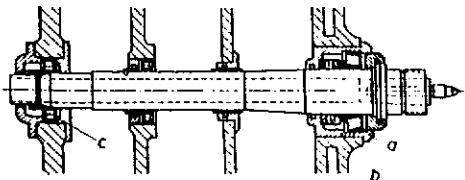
Husillo principal con cojinetes de deslizamiento: a) husillo principal; b) cabeza de husillo; c) cojinete; d) tuerca anular; e) cojinete de bolas para empuje axial.
